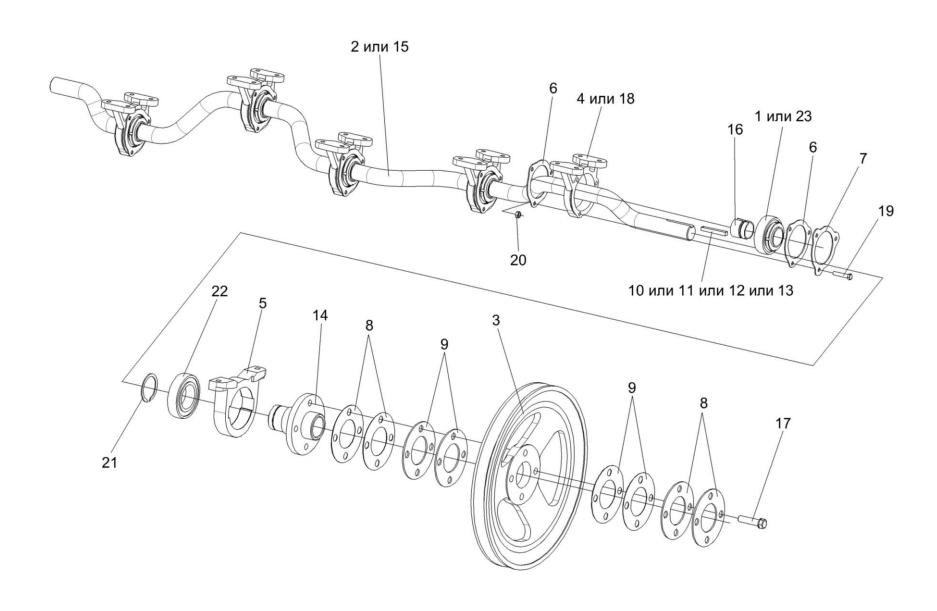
Вал коленчатый ведущий КЗК-12-0212070
